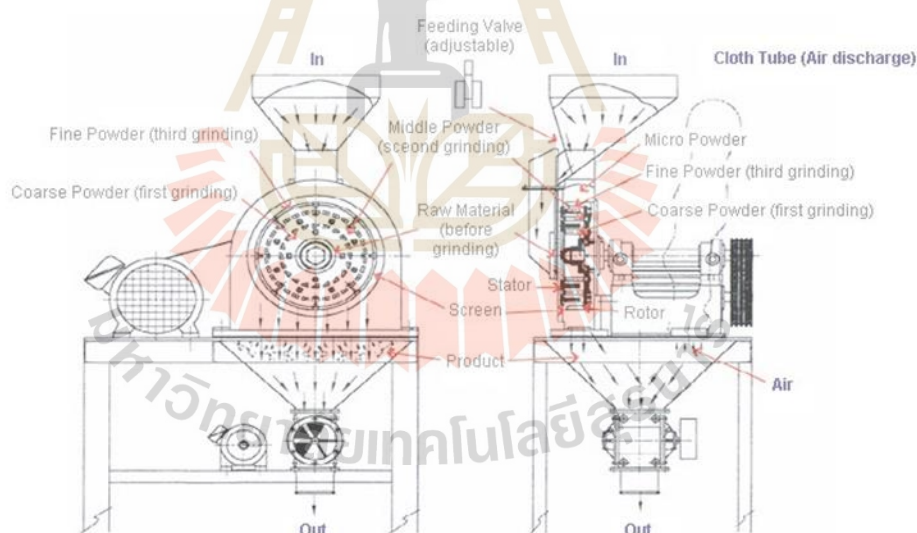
เครื่องบดแบบ Cutting Mill
